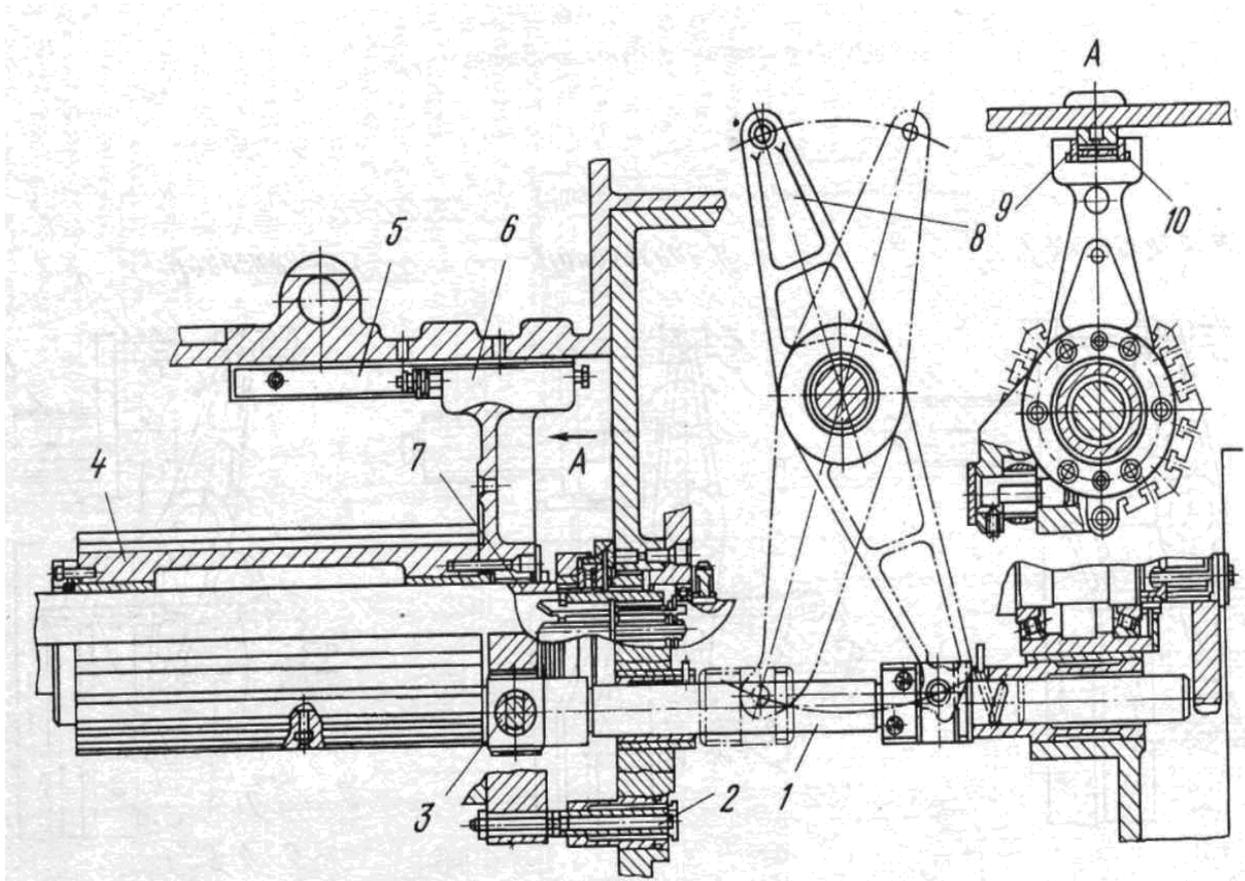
Продольный суппорт шестишпиндельного автомата.
